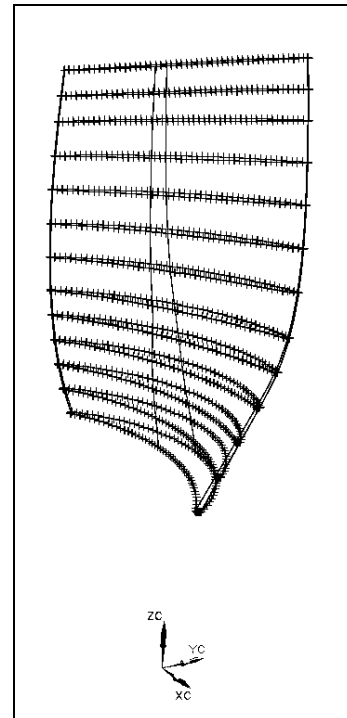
Профиль сечений колеса 1-й ступени КНД
